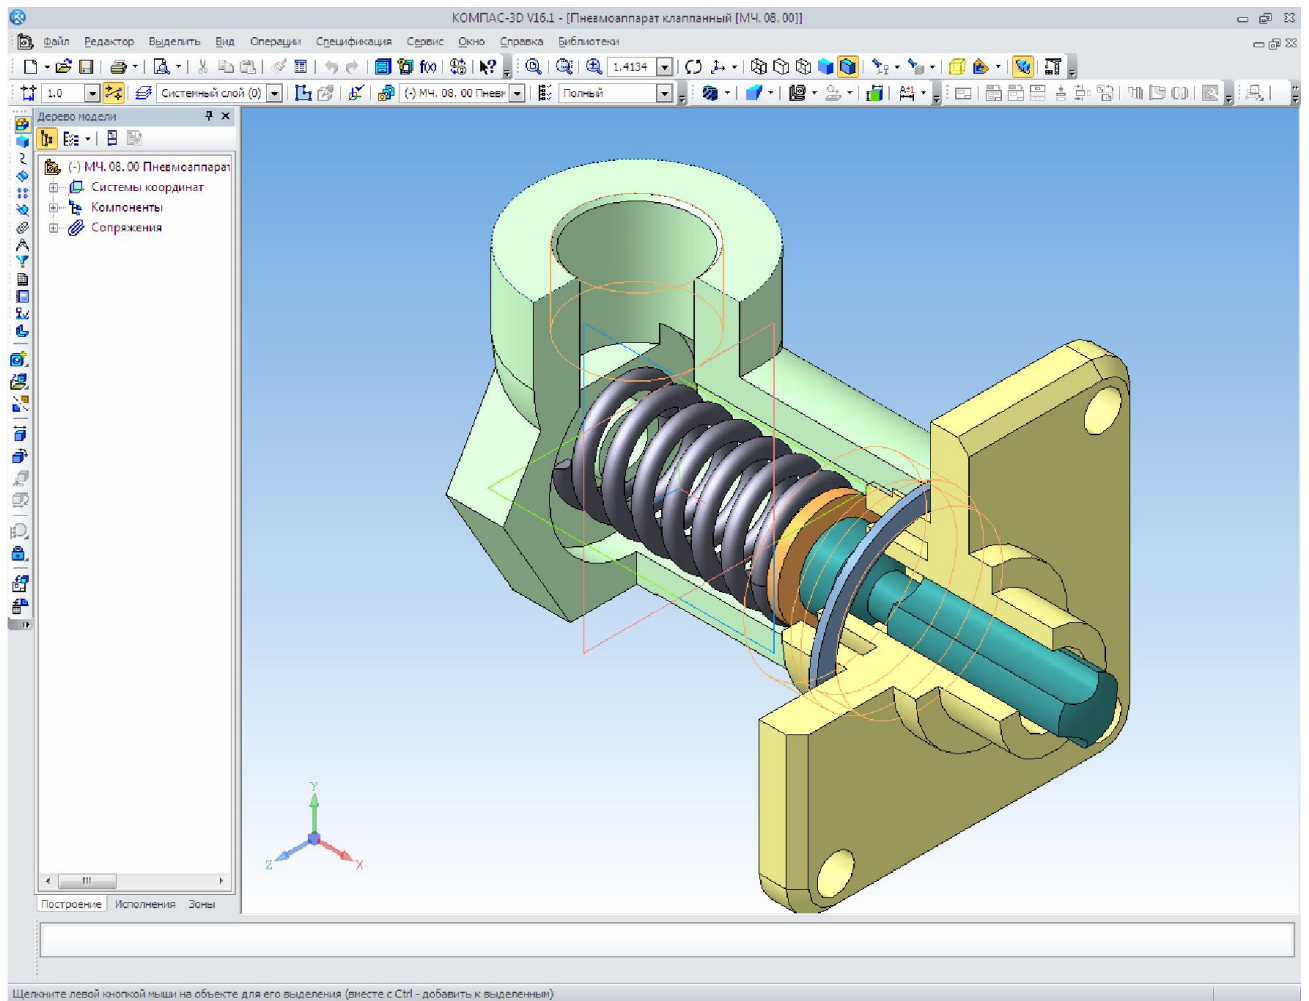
Пневмо аппарат клапанный, 3D сборка – общий вид
